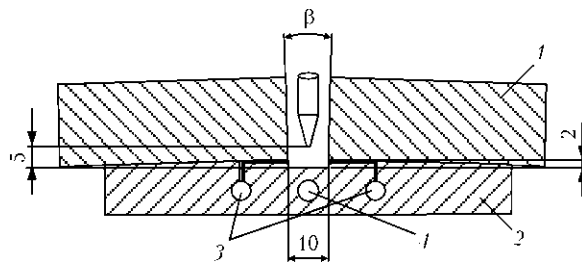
Схема сборки деталей под сварку: 1 — свариваемые плиты; 2 — формирующая подкладка; 3, 4 — соответственно отверстия для подачи защитного газа и протока охлаждающей воды
